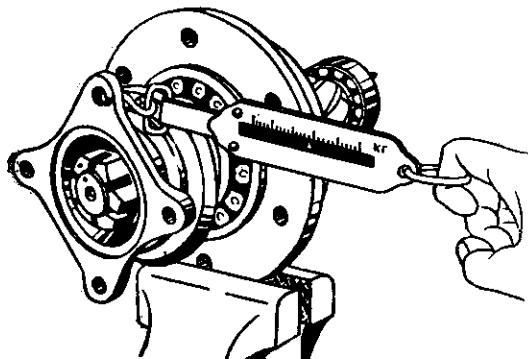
Проверка затяжки подшипников ведущей шестерни
